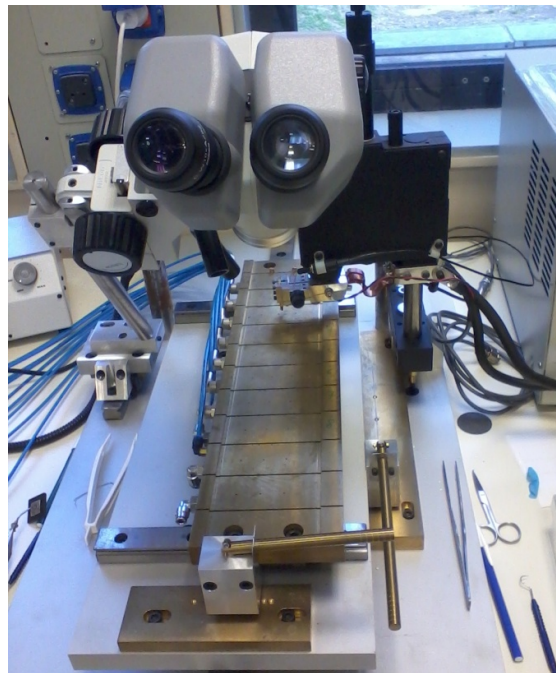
Posicionador de celdas CICs para la soldadura del interconector en la cara posterior para el armado de cadenas de celdas.
